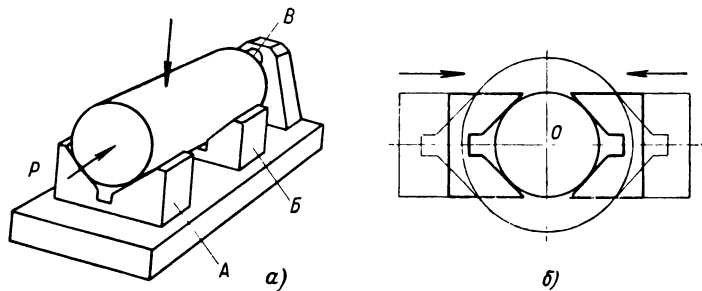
Схемы базирования заготовки по цилиндрической поверхности:
